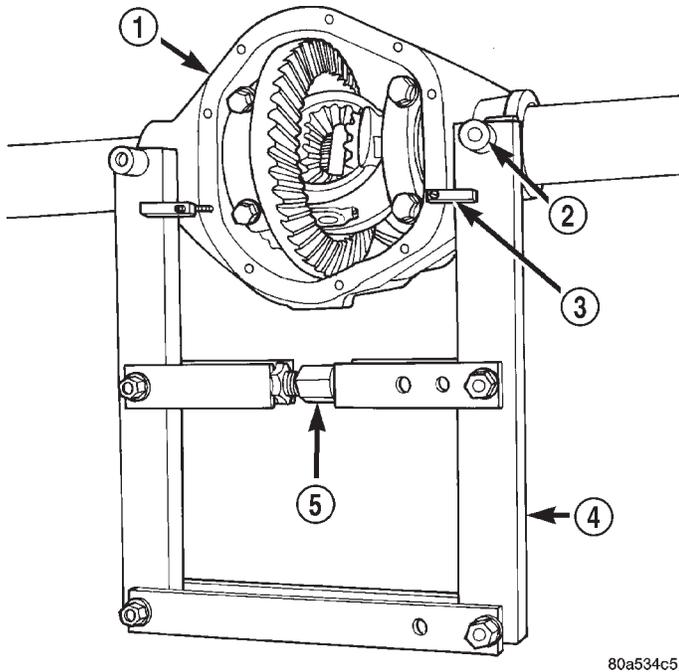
Spreizwerkzeug für Achsgehäuse installieren
